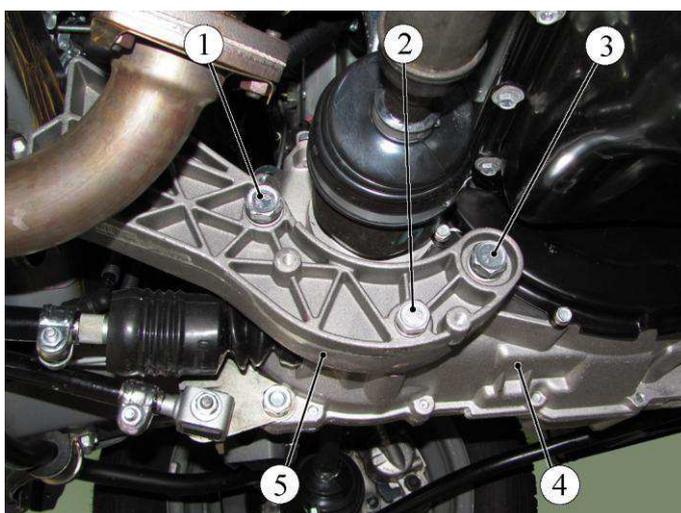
Отсоединение кронштейна задней опоры подвески двигателя от коробки передач:
